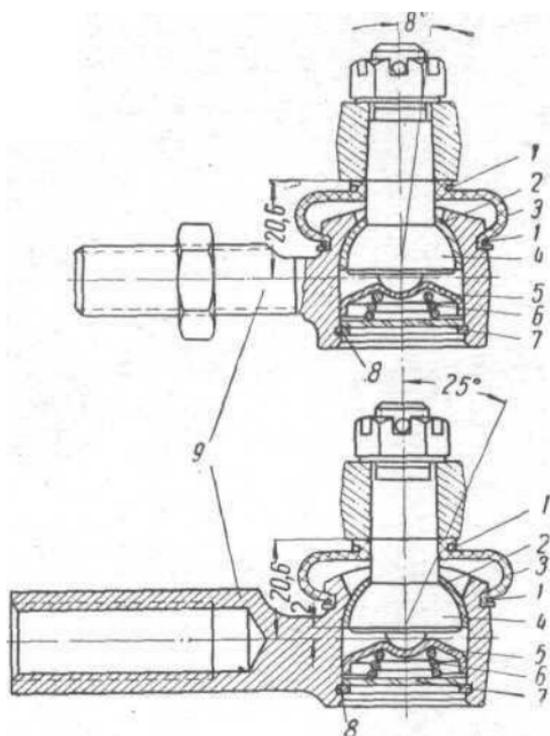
Шарниры рулевых тяг автомобиля модели 407 (вверху правый шарнир правой тяги, внизу шарнир левой тяги): 1— стяжное кольцо; 2— опорный вкладыш; 3— грязезащитный чехол; 4— шаровой палец; 5— нажимной вкладыш; 6— пружина; 7— заглушка; 8— стопорное кольцо; 9— наконечник
